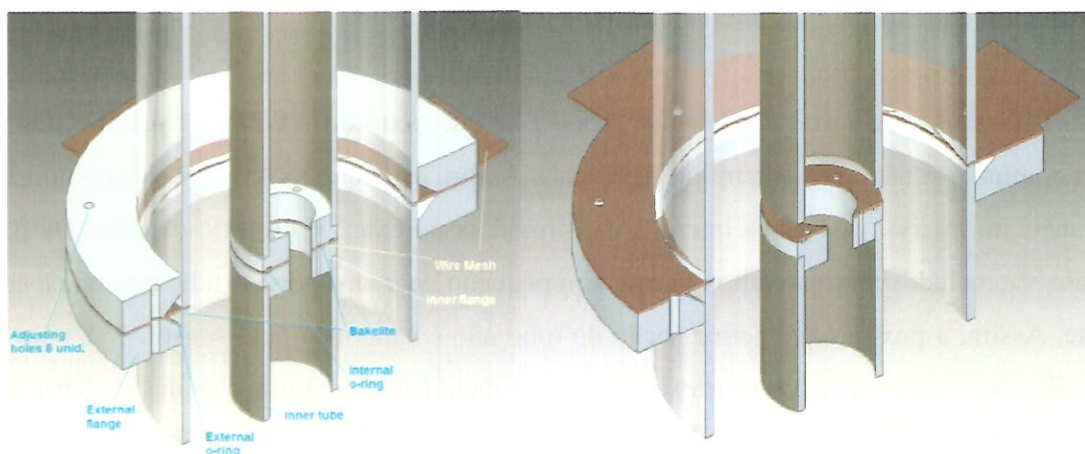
a) Corte transversal e detalhe do flange inferior com seus anéis e b) detalhe da posição do AWMS.
